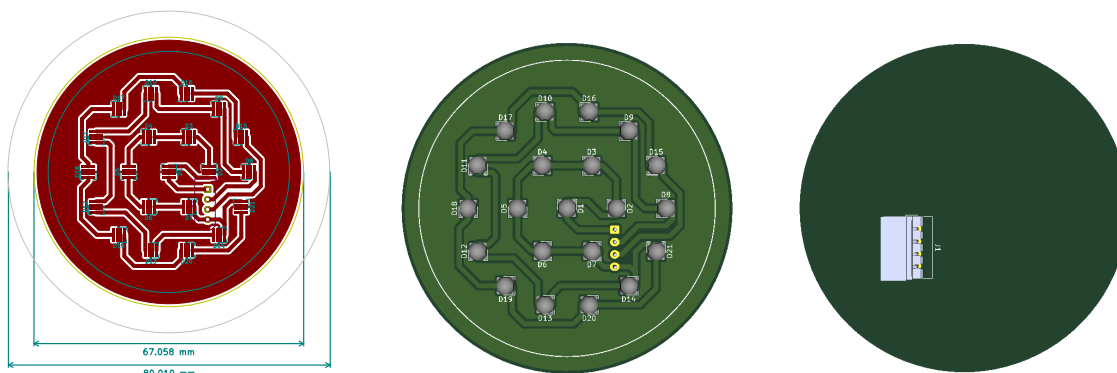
Dimensões e ilustração 3D da nova PCB de iluminação.
